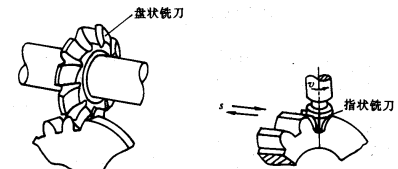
用盘状铣刀和指状铣刀铣齿轮
